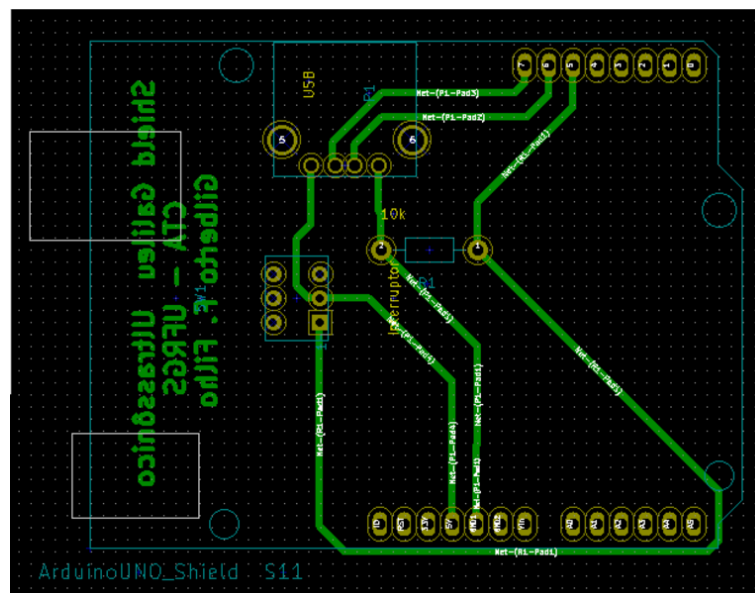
Desenho da placa *Shield Galileu Ultrassônico*.
